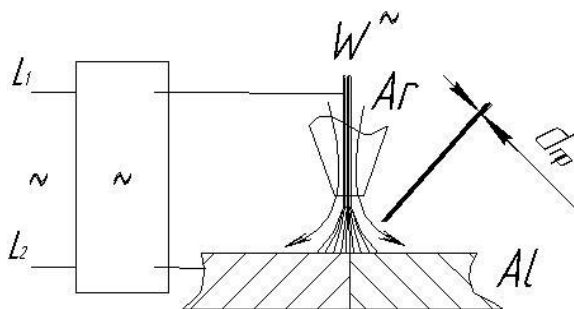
Схема сварки в импульсном режиме
